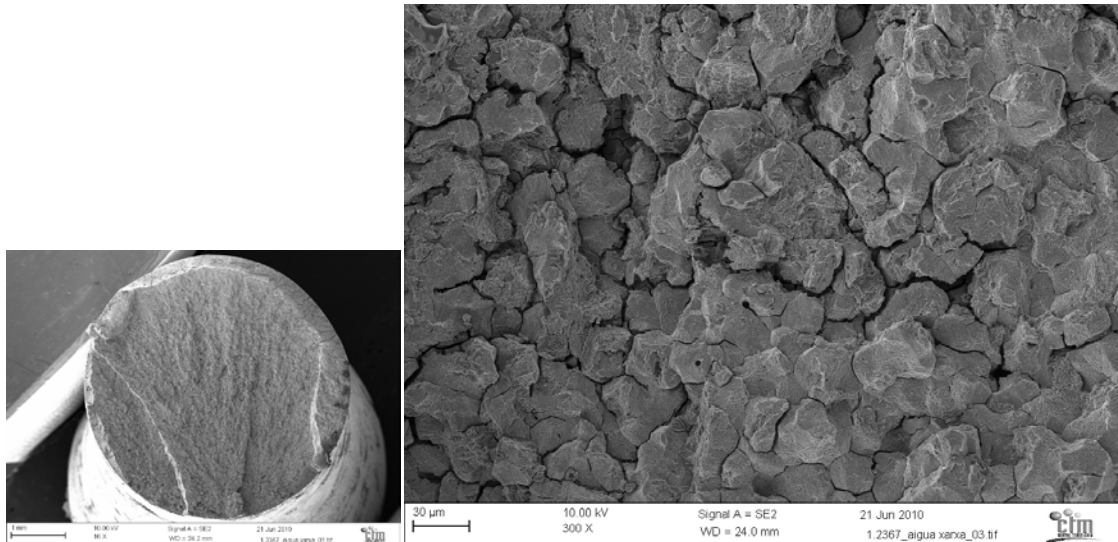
Superfície de fractura i zona d'inici de fractura per l'acer 1.2367 en aigua de xarxa a 80°C
